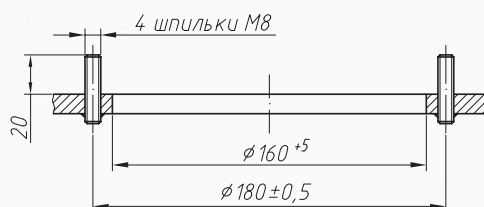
Эскиз доработки крышки резервуара для установки ППП1 (АПЖ) на одном фланце
